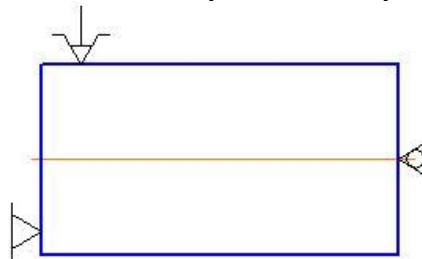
Схема закріплення в трьохкулачковому патроні з обертовим заднім центром з упором у торець
